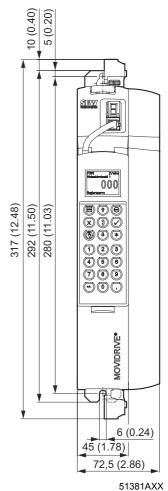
Dimensões MDX61B, tamanho 0S, dimensões em mm (in)
